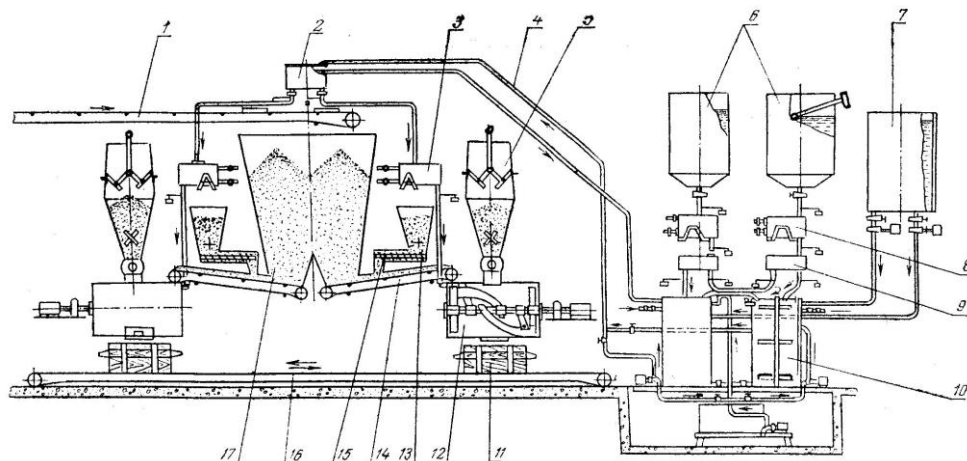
Схема установки лопаткового змішувача для приготування самотвердіючих сумішей
